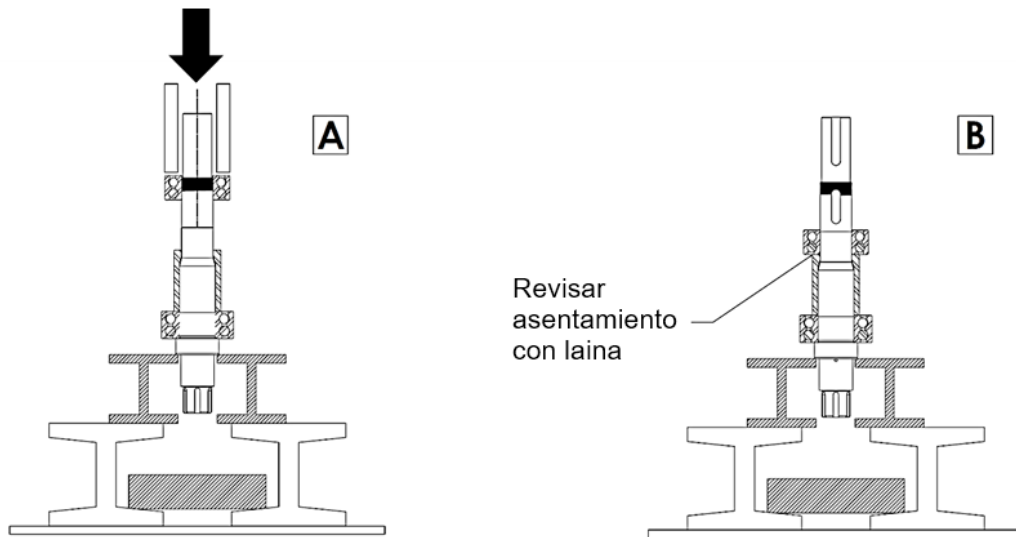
Presión del rodamiento delantero sobre la flecha
